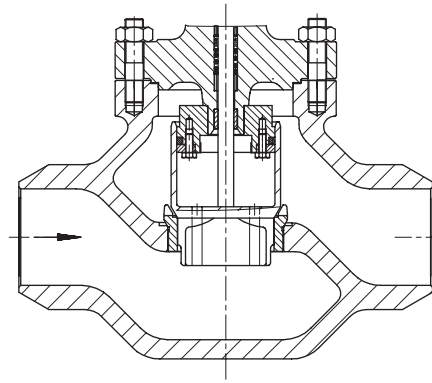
· Válvula Tipo 3251 com extremidades soldadas e obturador equilibrado da válvula
